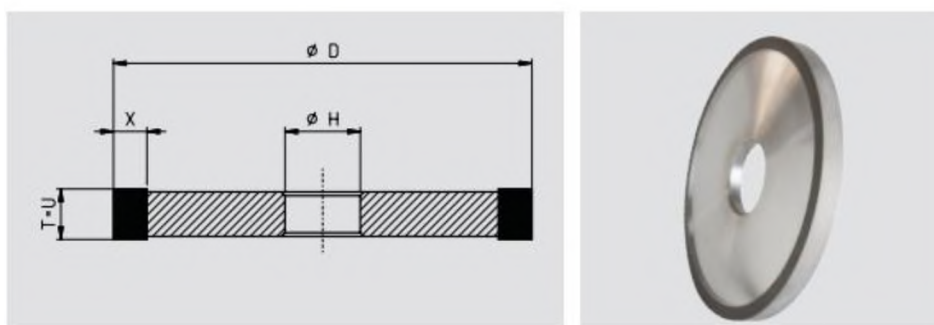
Шліфувальний круг [2, стр.115]
